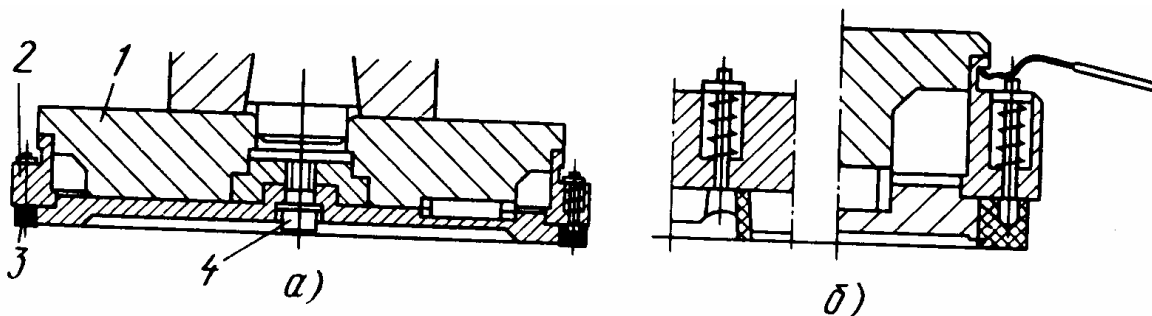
Торцева фреза з твердосплавними пластинами закріпленими за допомогою підпружинених пальців: а – фреза; б – вузол кріплення
